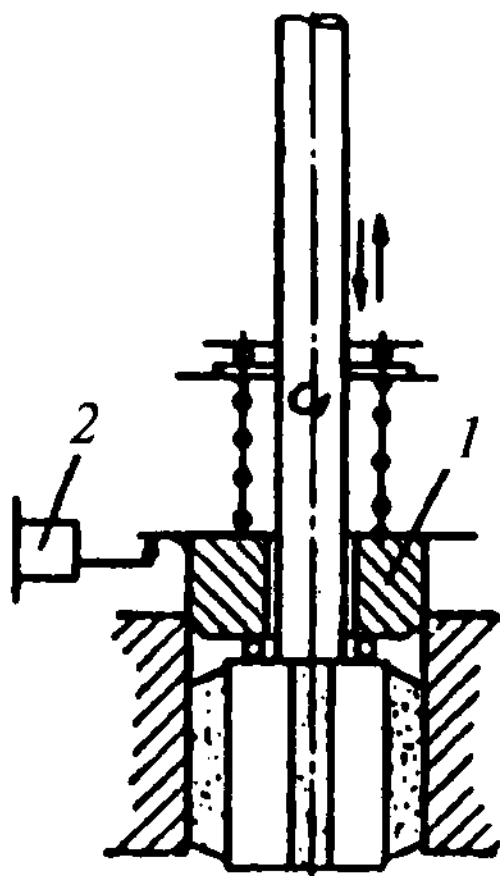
Схема измерительного устройства для хонинговального станка
